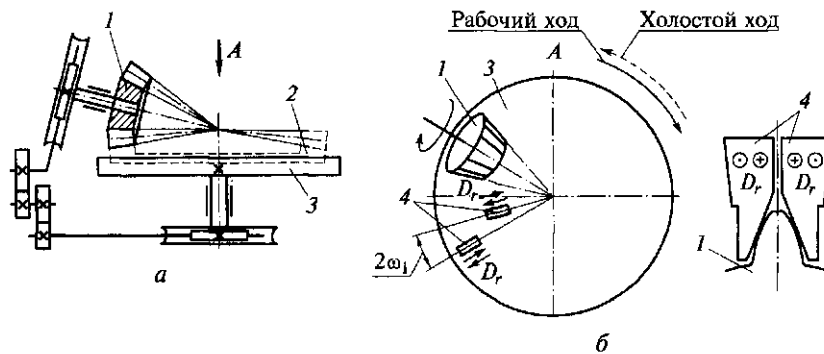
Принципиальная схема нарезания зубьев конического колеса впадиной производящего колеса (а) и формирования впадины резцами (б): 1 — заготовка; 2 — производящее колесо; 3 — люлька; 4 — резцы;  $2\omega_1$  — угол установки резцов (ползунув)
